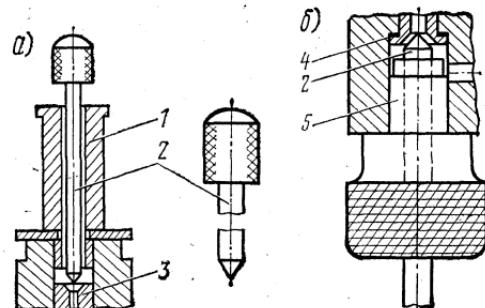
Фрезеровка верхнего седла включающего вентиля (а) и нижнего (б):
